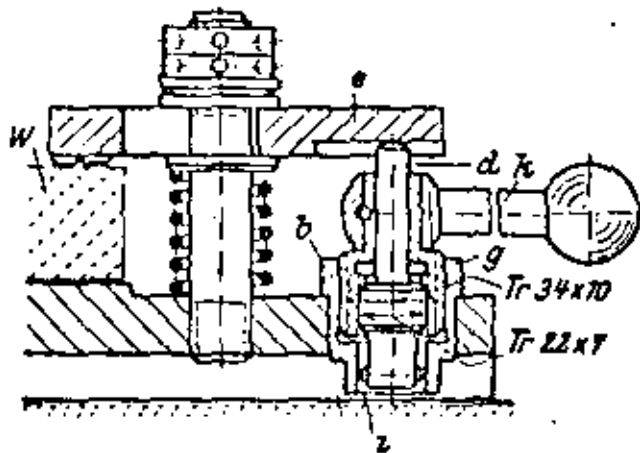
Tensor de correa con rosca doble. Tr 34x10 doble paso a izquierdas. Tr 22x7 doble paso a derechas. Carrera para 1/4 de vuelta, 0,25 mm
